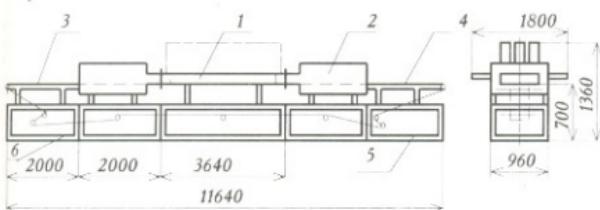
СВЧ-линия для медленного вспучивания сырьевой смеси: 1 — СВЧ-камера; 2 — шлюз; 3, 4 — разгрузочный и загрузочный столы; 5 — привод; 6 — натяжная станция конвейера
